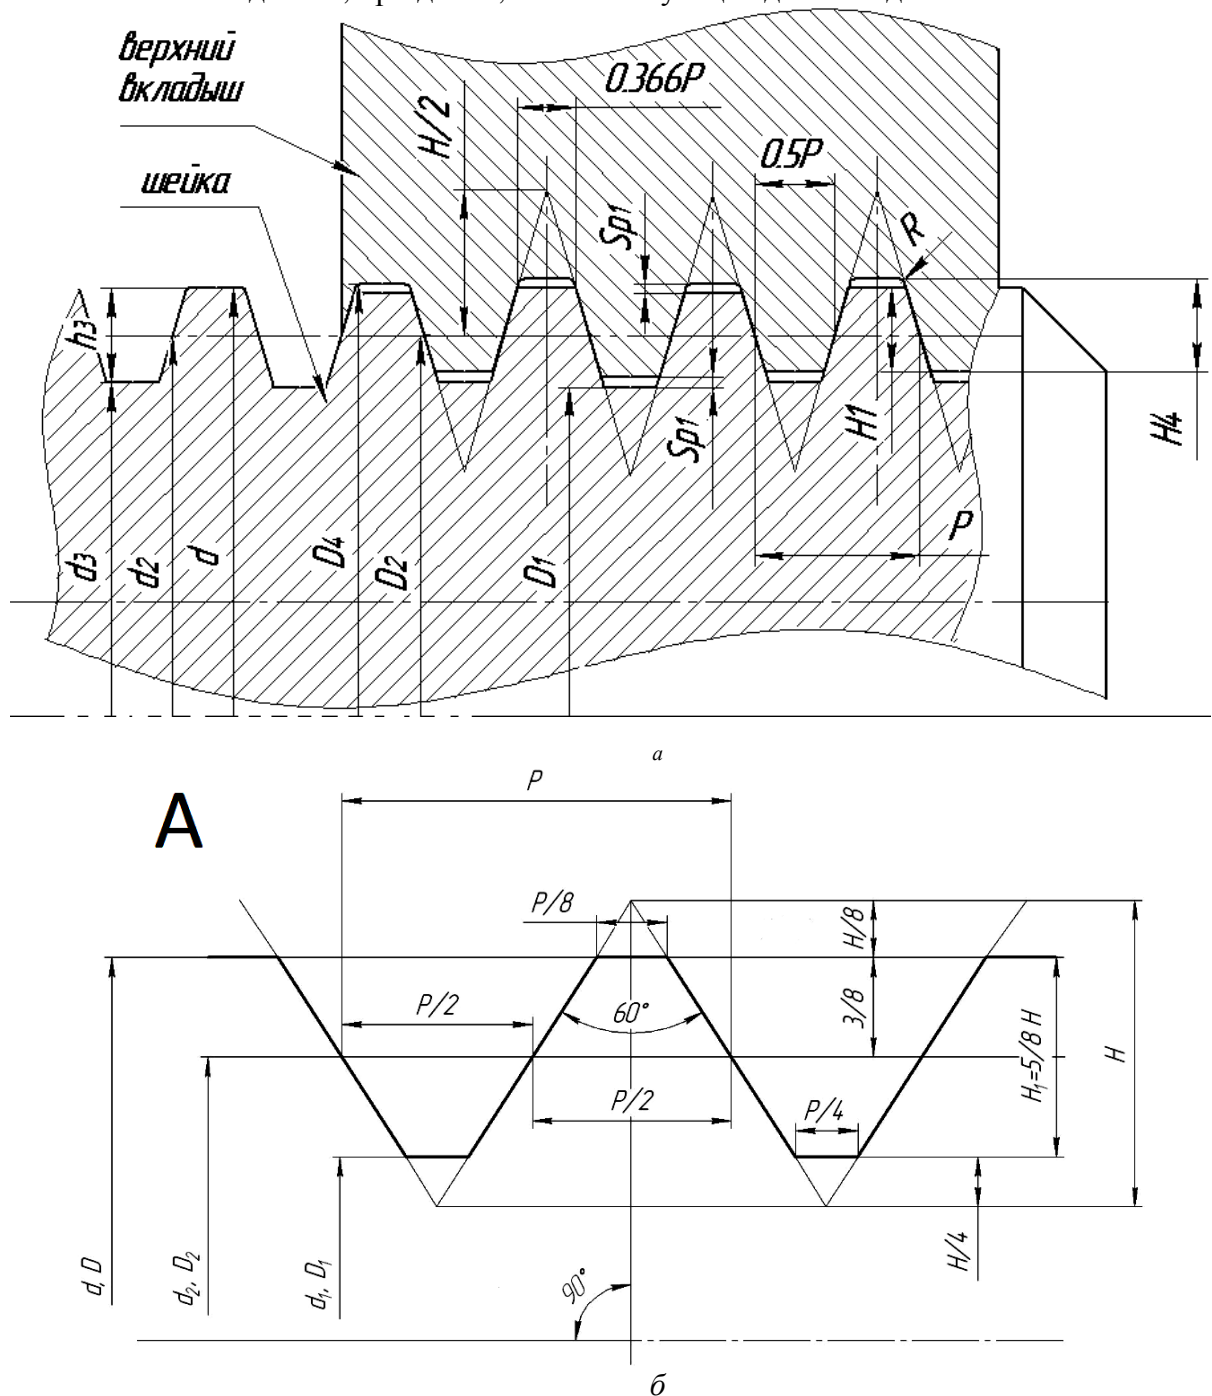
Схема геометрических параметров макрорельефов: а – вид РПП трапецеидальной формы, содержащей сборный подшипник и шейку вала; б – профили контактирующих поверхностей РПП треугольной формы, H – высота исходного треугольника, $H = 0,866P$, $H_1 = 0,541P$; $3/8H = 0,325P$; $H/8 = 0,108P$; $H/4 = 0,216P$
